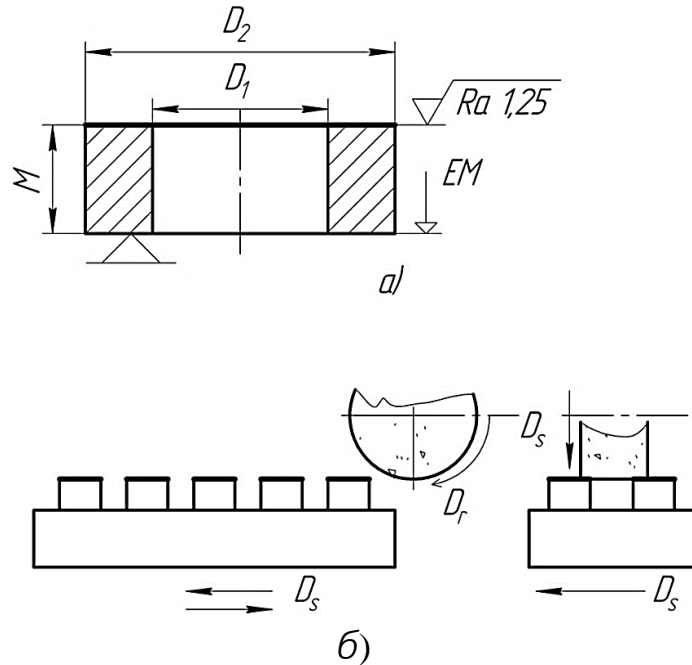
Схема оброблення: а) – ескіз оброблення; б) – схема налагодження
